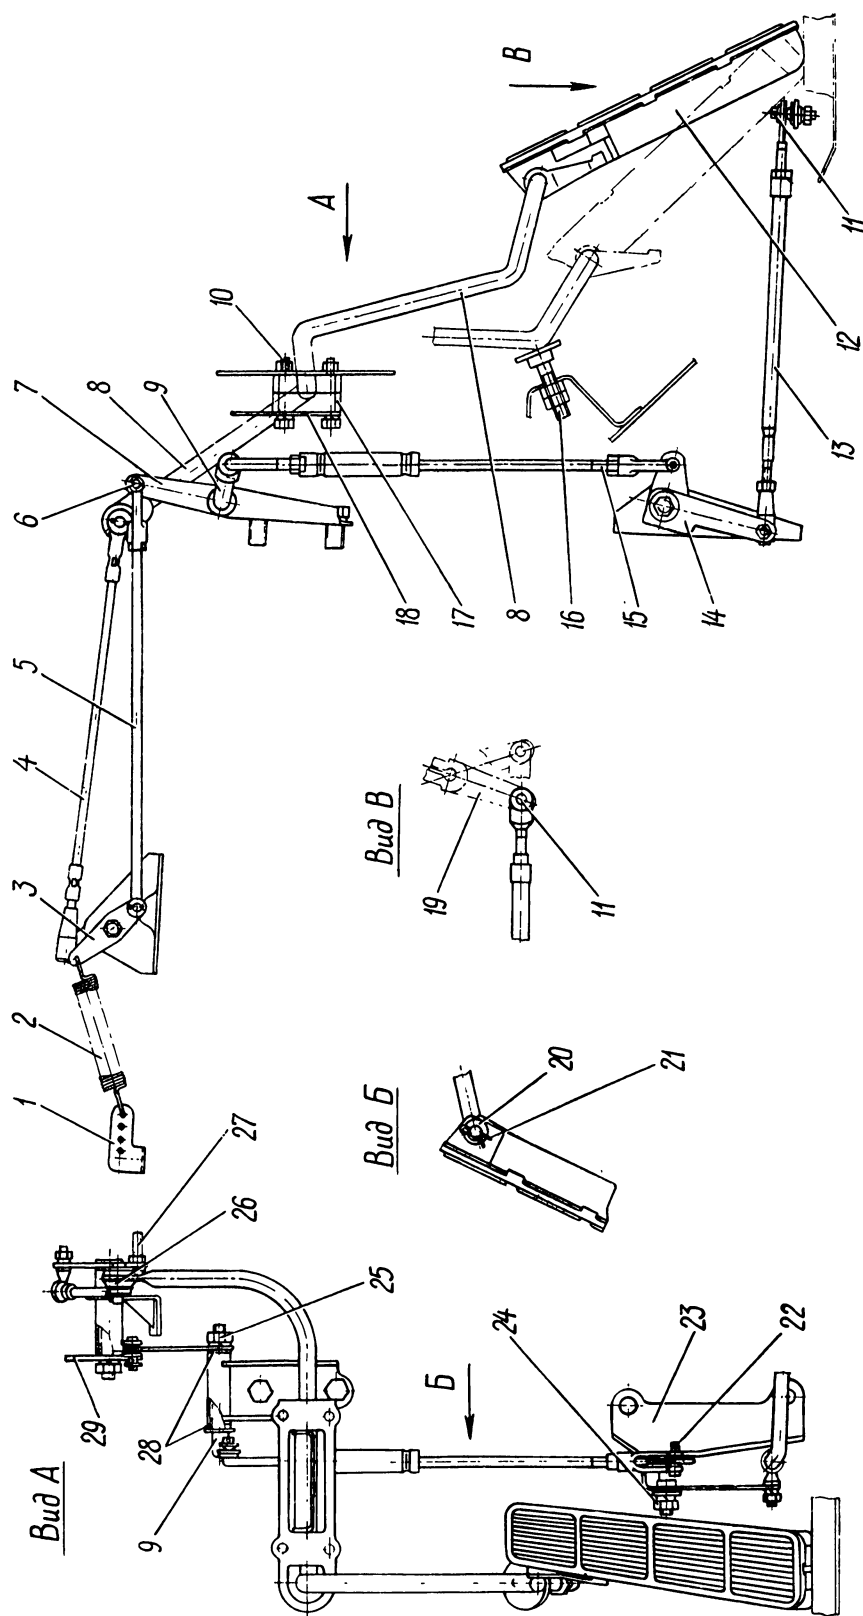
Привод силового регулирования коробки передач и управления карбюратором
